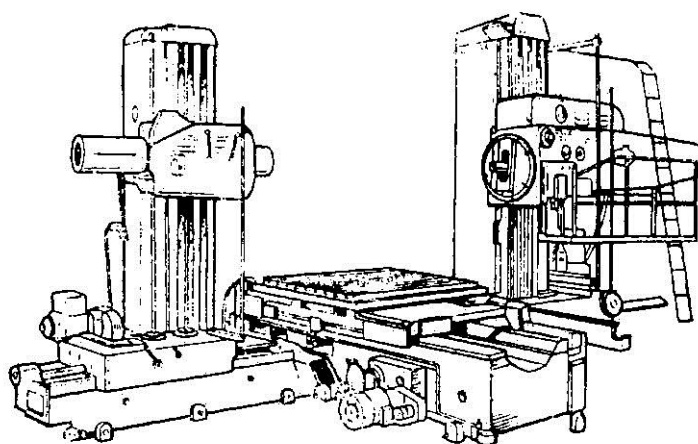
Горизонтально-розточувальний верстат (мод. 2654)
